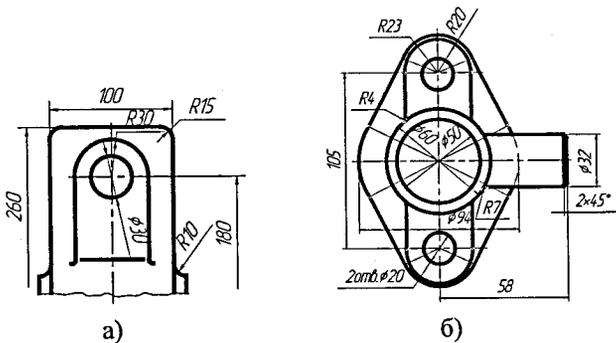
Спряження на корпусах підшипника (bearing body)
